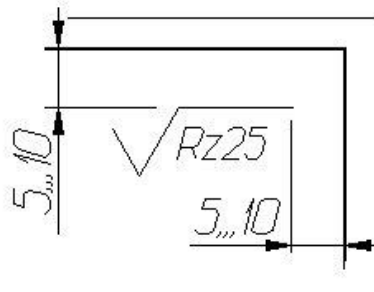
Пример обозначение шероховатости, одинаковой для всех поверхностей изделия
